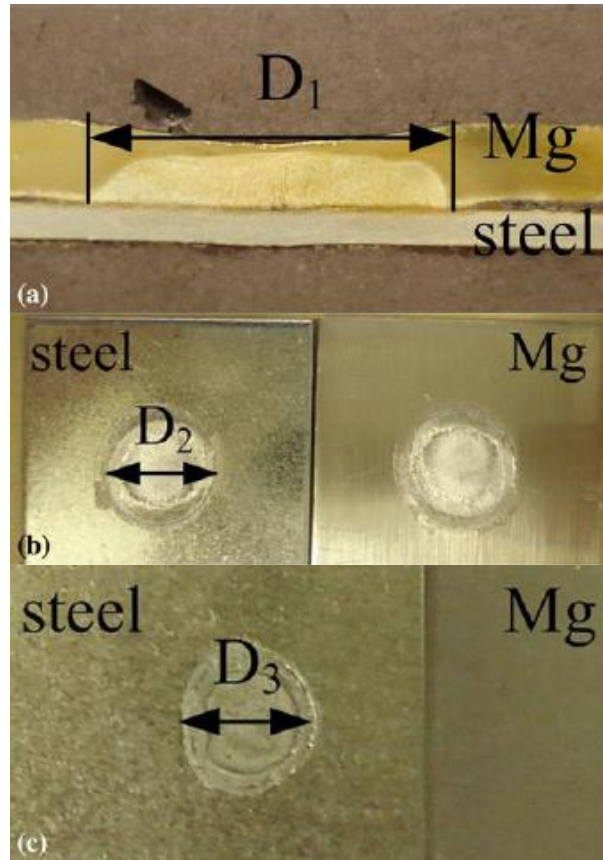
Medidas de las dimensiones de soldadura con los siguientes métodos: a) Sección transversal de la soldadura, b) Fractura de superficie, y c) Zinc fundido en la interfaz del Acero [16].
